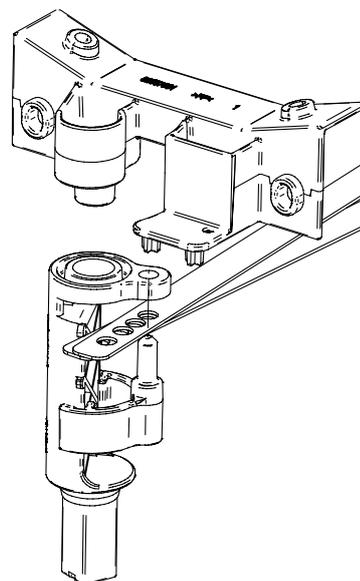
Il est également possible de verrouiller un côté, par exemple.
